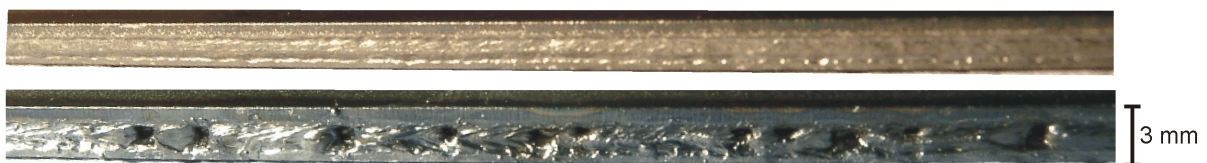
Optische Begutachtung der Schweißnaht
